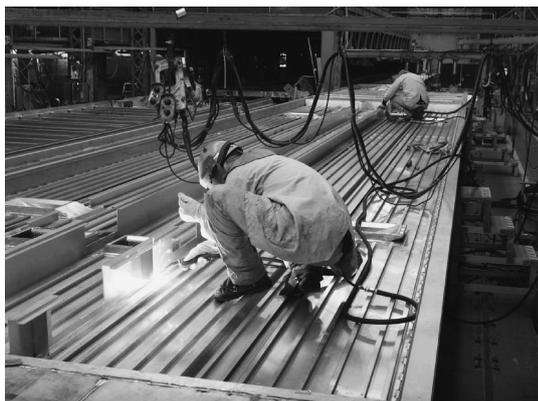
アルミ構体の台枠パネルをMIG溶接で施工
